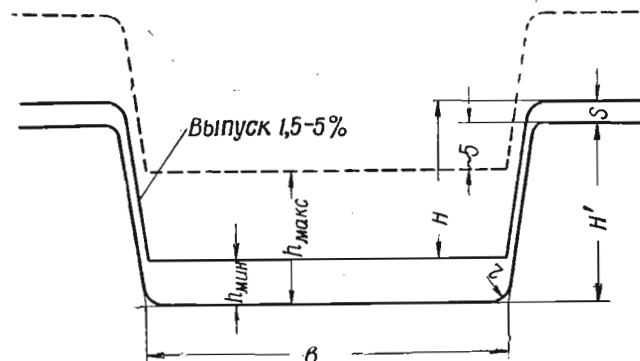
Конструкция закрытого калибра для прокатки полосовой стали
